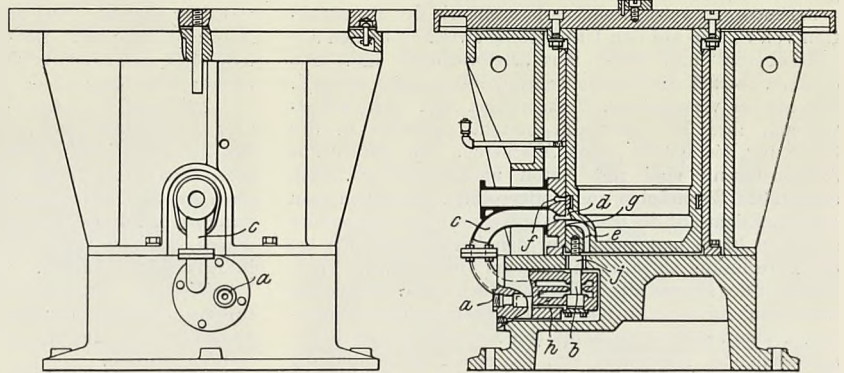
Steuerung der Mumford-Rüttelformmaschine.
